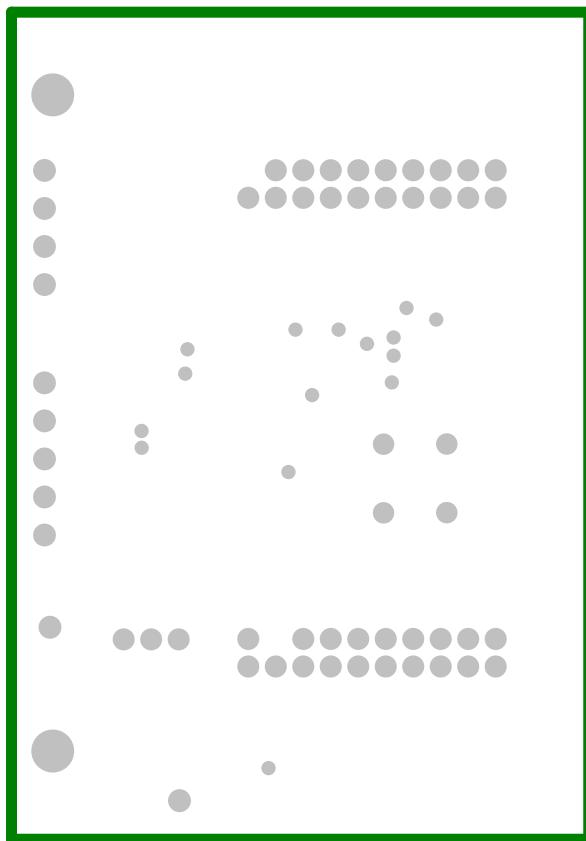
ADS122x14EVM の PCB レイアウト (内部 GND プレーン 1)
